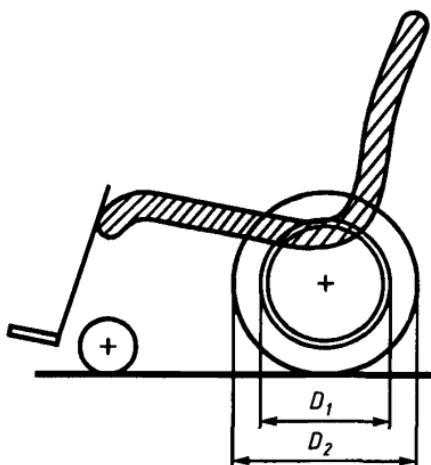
Диаметр ручного приводного обода и диаметр ведущего колеса
